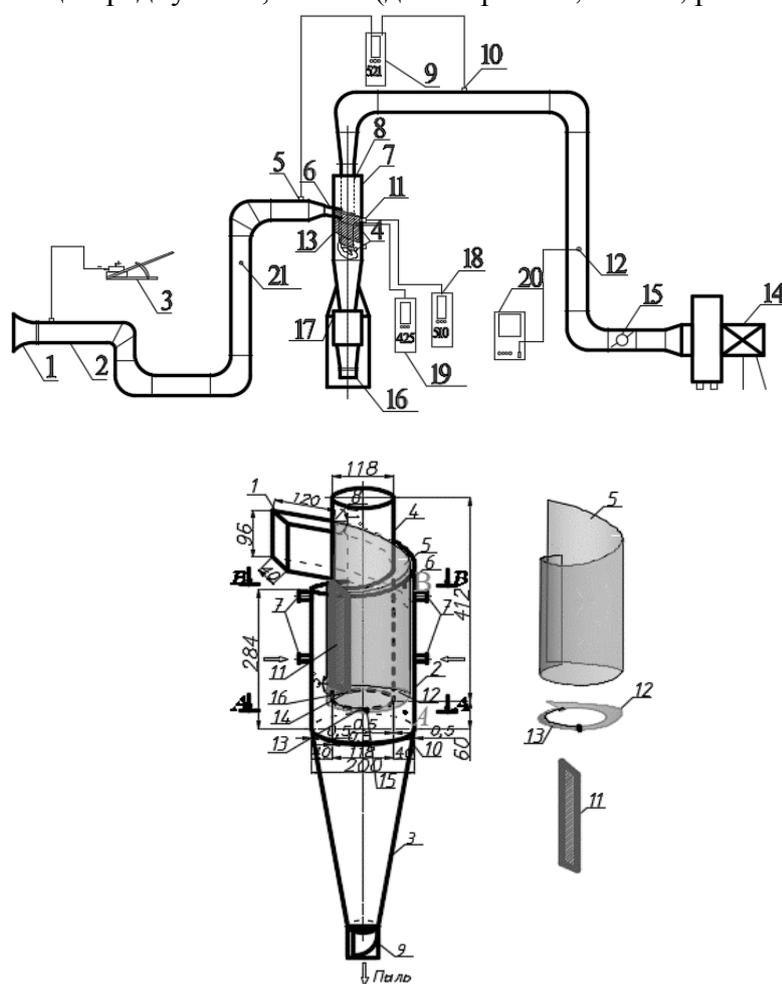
Схема конструкции циклона-фильтра: 1 – входной патрубок; 2 – цилиндрический корпус; 3 – коническое днище; 4 – выхлопная труба; 5 – фильтровальный материал; 6 – металлический каркас; 7 – продувочные штуцера; 8 – торец циклона; 9 – заслонка; 10 – детали крепежа; 11 – поперечный фильтр; 12 – горизонтальный фильтр, тканая часть; 13 – горизонтальный фильтр, металлическая часть; 14 – пластина с пружиной; 15 – стержень с кольцами; 16 – складывающийся фильтр
